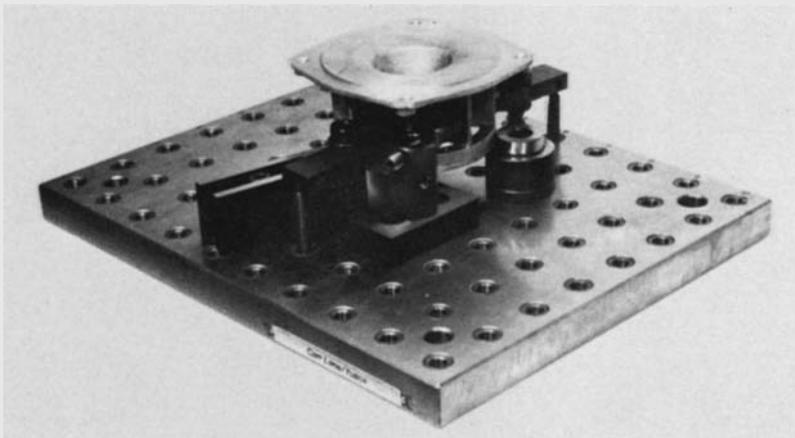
Soporte modular terminado con la carcasa de hierro fundido en su lugar, como se ensamblaría para uso en un centro de maquinado o fresadora CNC. *Fuente:* Cortesía de Carr Lane Manufacturing Company.
